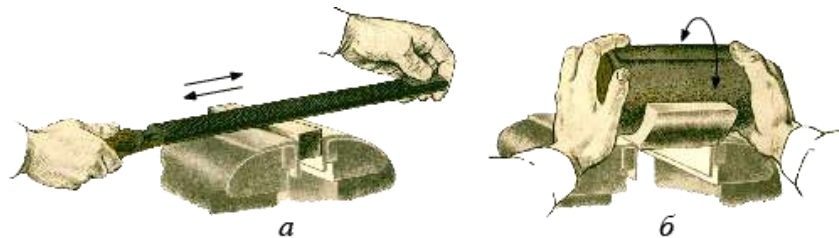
Обробка начисто обпиляної поверхні:
